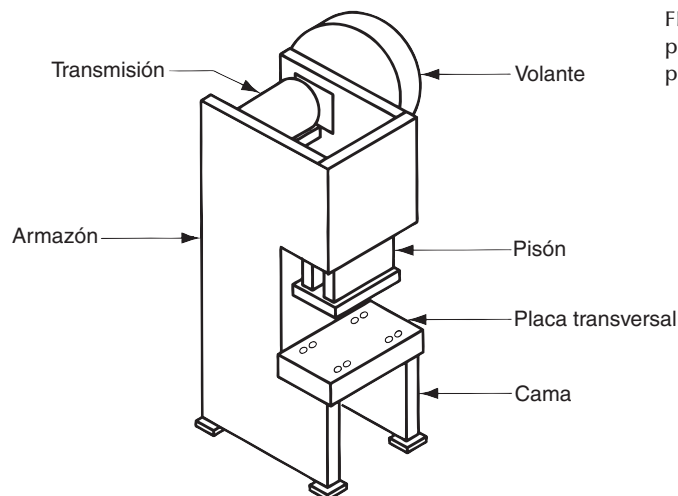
Componentes de una prensa troqueladora típica accionada por transmisión mecánica.
